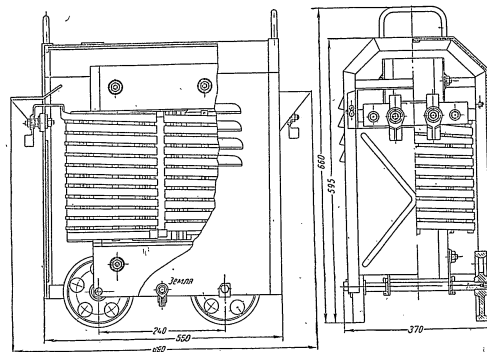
Общий вид и габаритные размеры трансформатора СТЭ-34
